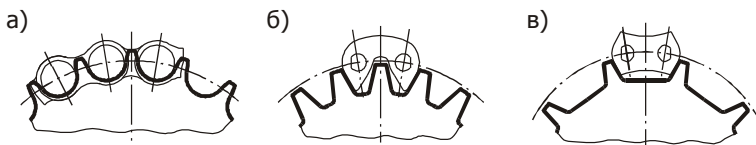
Зацепление звездочки с цепью: а – роликовой; б – зубчатой типа 1; в – зубчатой типа 2
